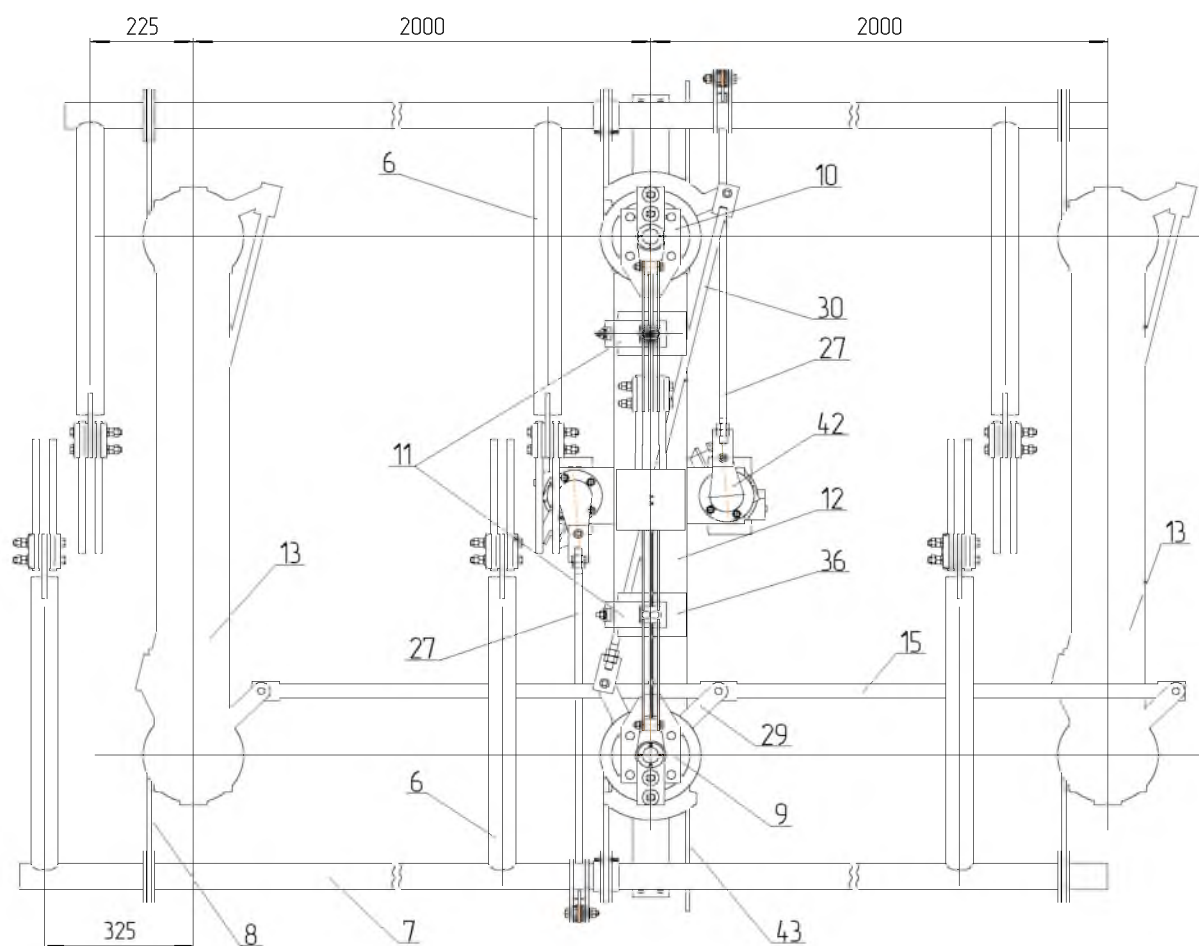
Разъединитель трёхполюсный РГП СЭЩ® -110
